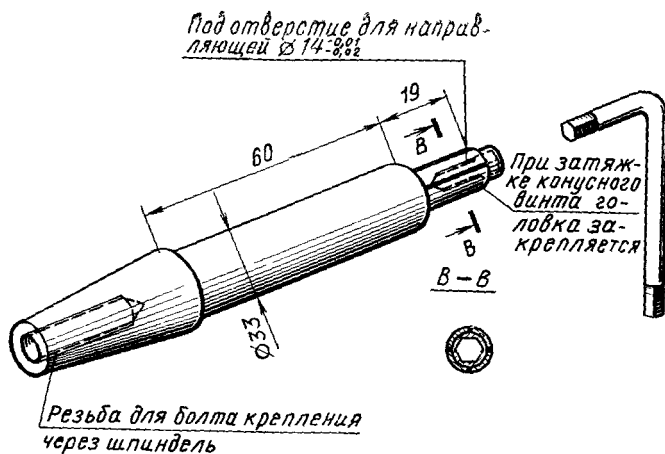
Приспособление для крепления головки при расточке гнезда под седло клапана на токарном станке
